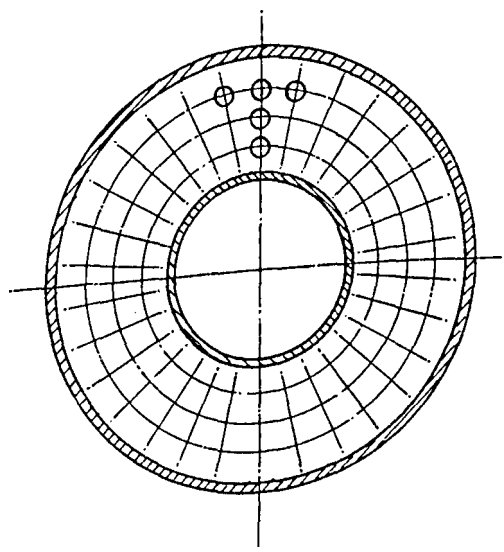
Placa perfurada de 3mm de diâmetro
